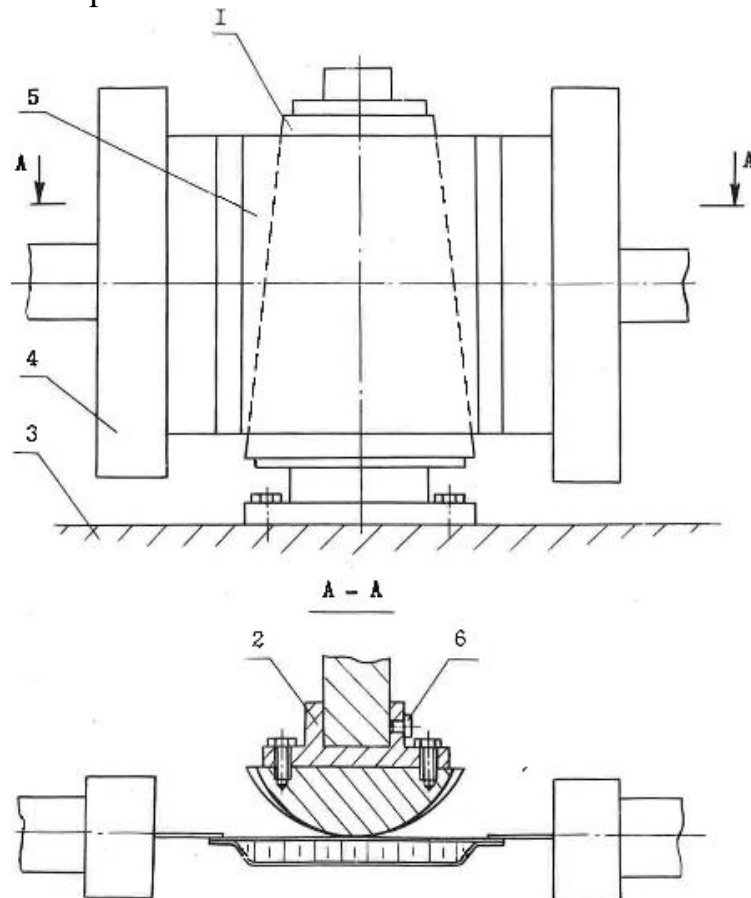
Схема положения пуансона и заготовки на прессе ГРП при предварительном растяжении: 1 – пуансон; 2 – каркас; 3 – стол пресса; 4 – зажим; 5 – заготовка; 6 – стопор.
